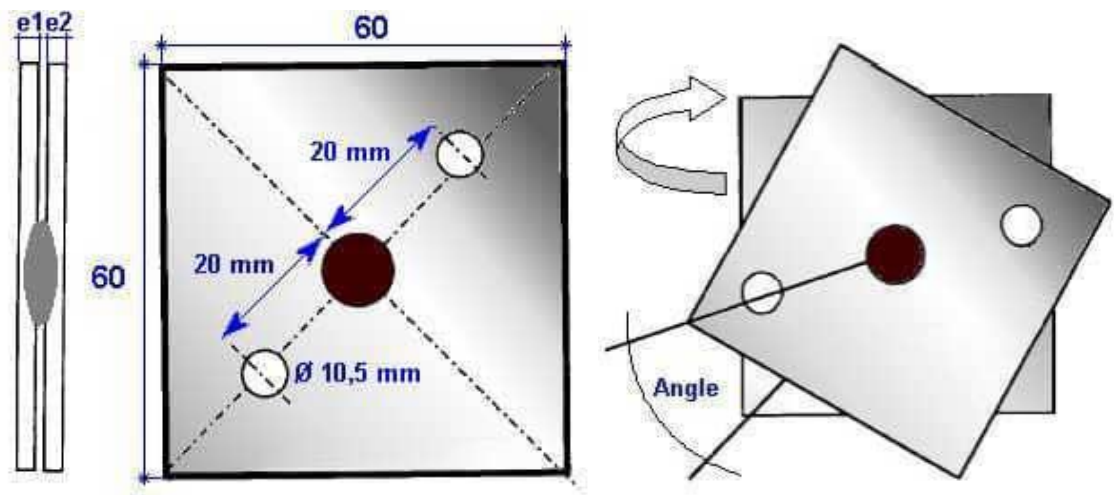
Essai de cisaillement par torsion du point soudé
